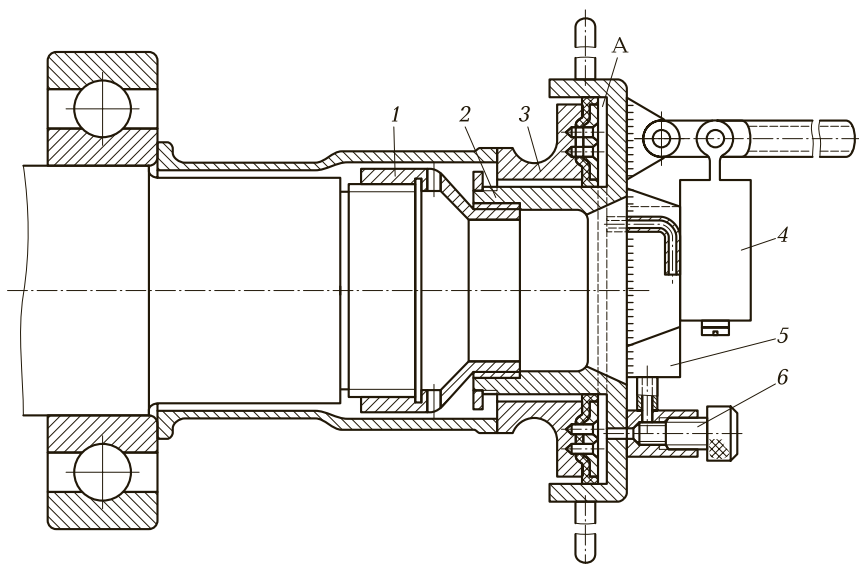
Приспособление с гидравлическим приводом для напрессовывания на вал крупногабаритных подшипников:
